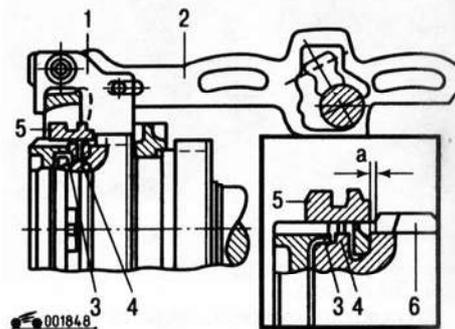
Элементы механизма включения V передачи: 1 – вилка включения V передачи; 2 – рычаг перемещения вилки V передачи; 3 – пружина; 4 – кольцо синхронизатора; 5 – скользящая муфта синхронизатора; 6 – шестерня; а – зазор, равный 1,2 мм
